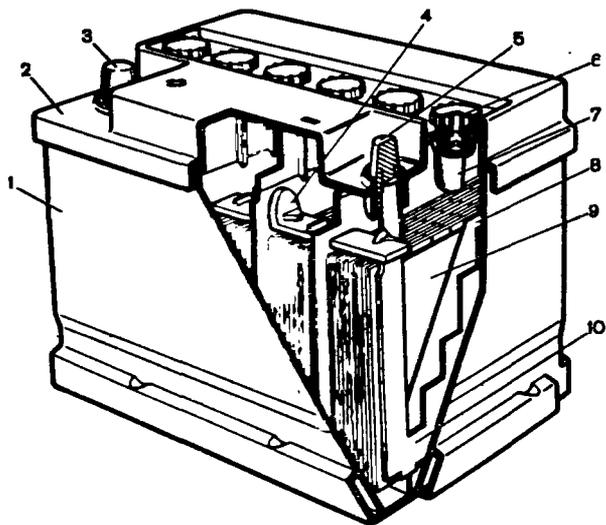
Разрез аккумуляторной батареи: 1 - корпус; 2 - крышка; 3 - положительный вывод; 4 - межэлементное соединение; 5 - отрицательный вывод; 6 - пробка; 7 - индикатор для проверки уровня электролита; 8 - сепаратор; 9 - положительная пластина; 10 - отрицательная пластина
